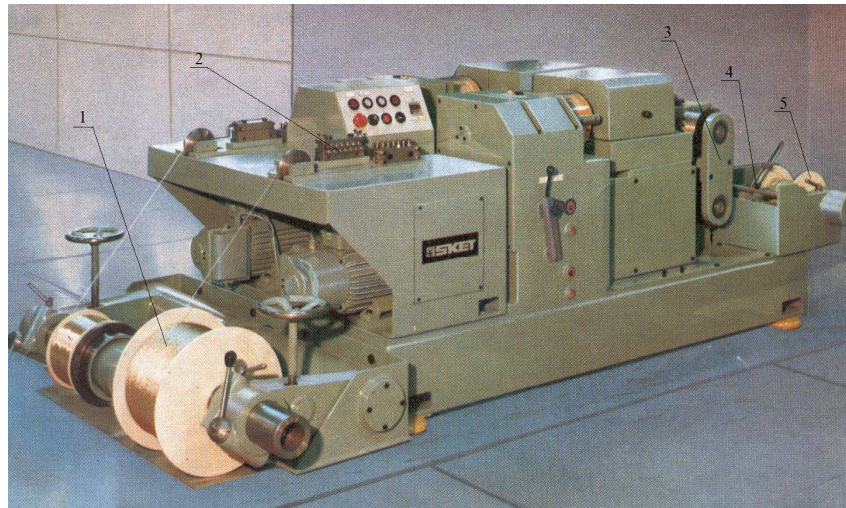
Внешний вид сдвоенного намоточного станка с общей несущей рамой:
